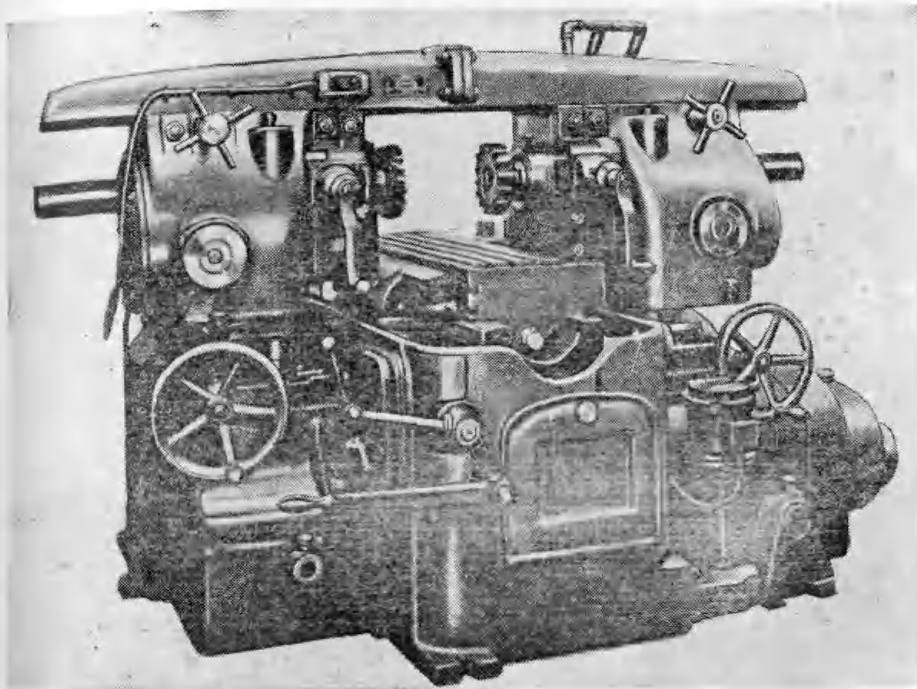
Широкоуниверсальный фрезерный станок мод. 678. Размер
